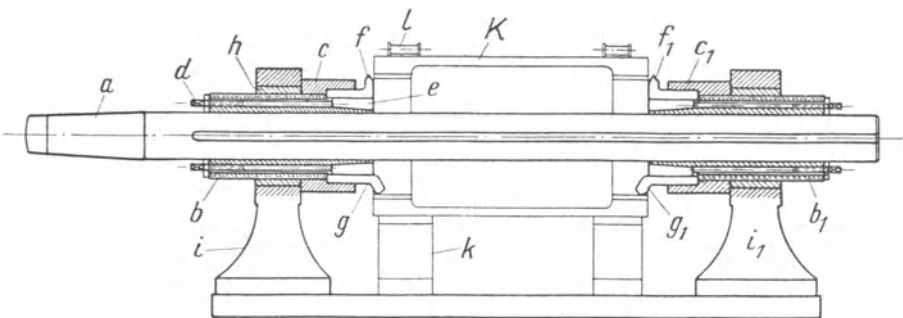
Ausbohr- und Gewindeschneidvorrichtung zum Bearbeiten schwerer Zylinderkörper.
